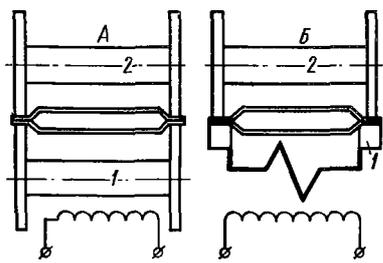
Схемы коротковитковых швновых машин для сварки кромочных швов
